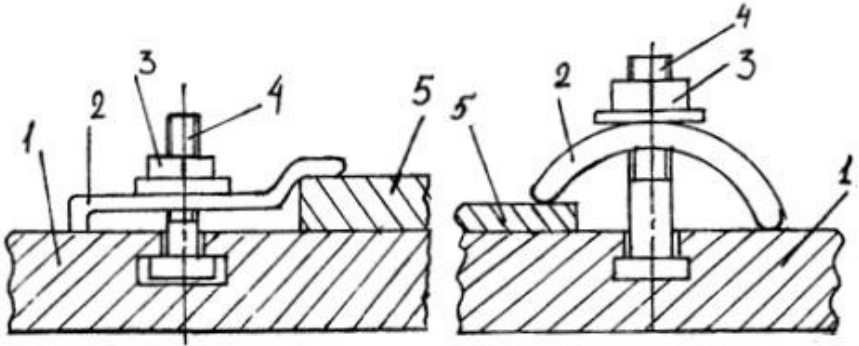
Закріплення заготовки на столі верстату за допомогою прихвату: 1 - стіл; 2 - прихват; 3 - гайка; 4 - болт; 5 – заготовка
